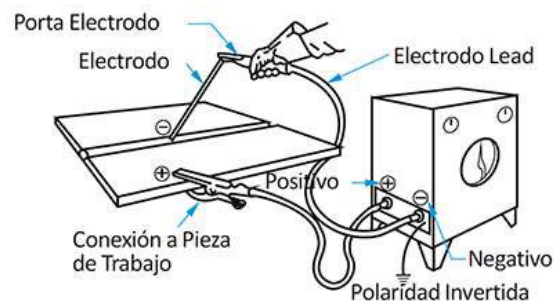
Equipo para el proceso de soldadura SMAW.
